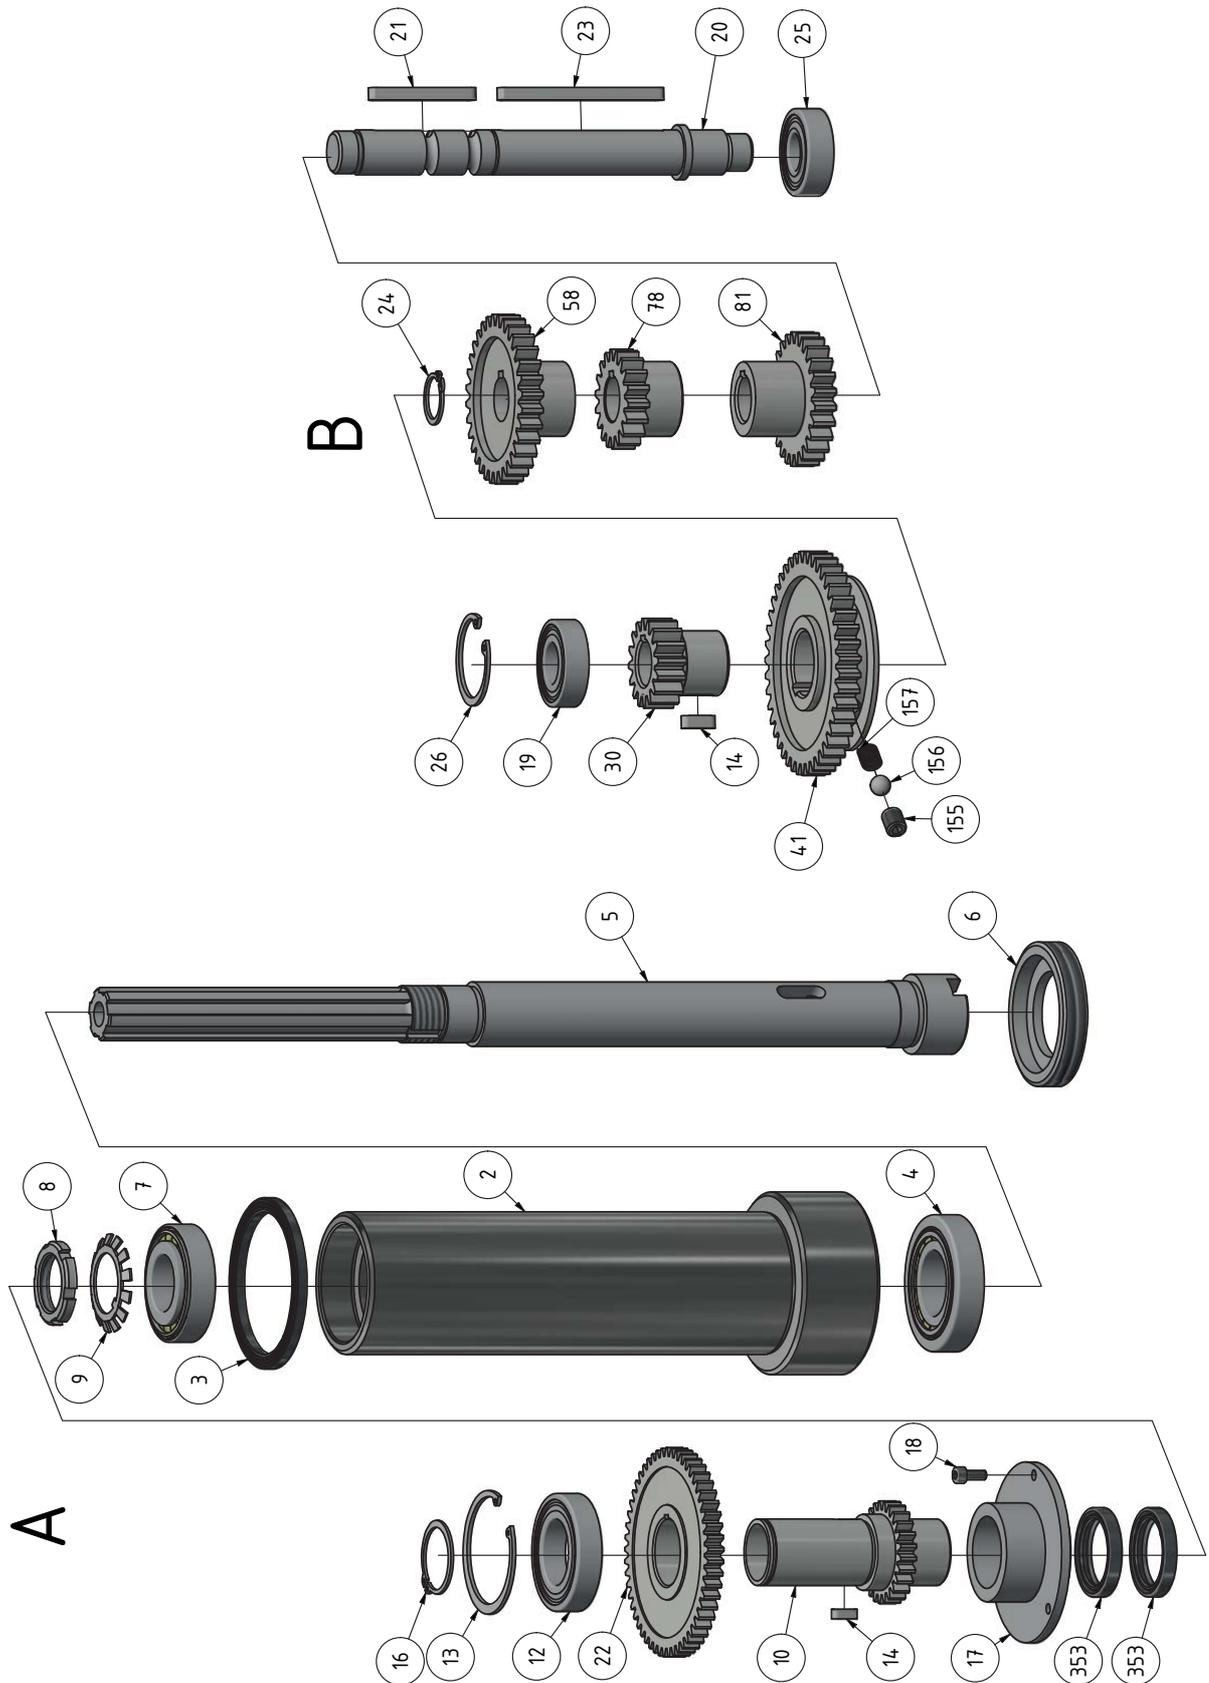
Fräskopf 2 von 6 - Milling head 2 von 6
